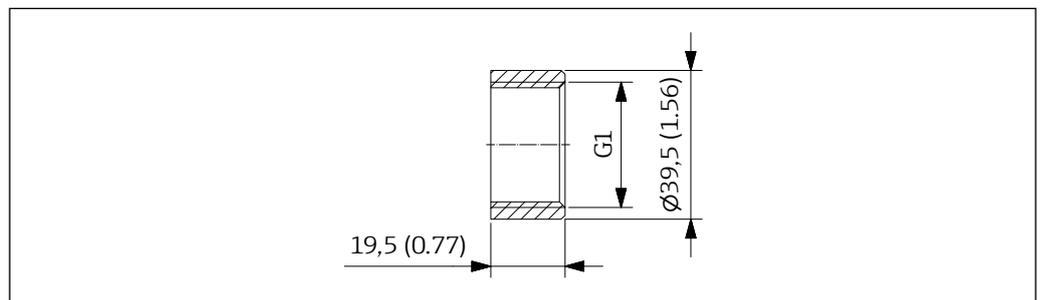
Dimensiones manguito de soldadura. Unidad de medida mm (in)
